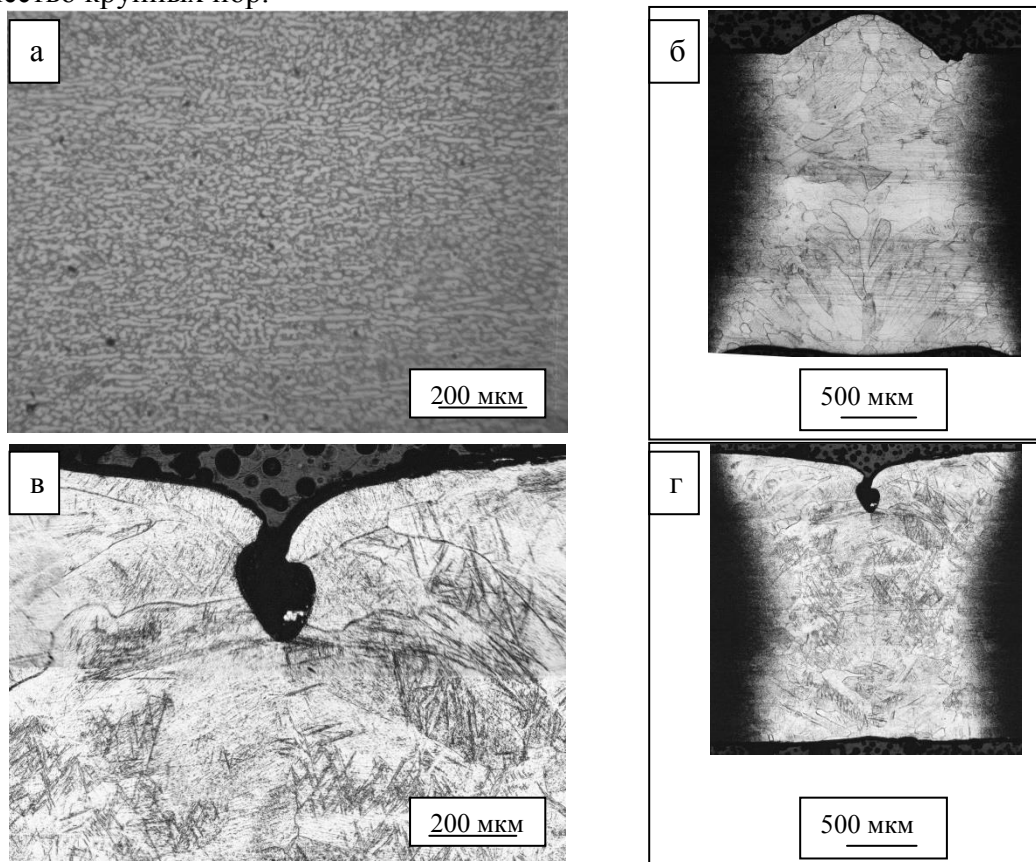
Структура сварных соединений титанового сплава BT23: а - зона основной металл без применения обработок; б - панорама сварного шва без применения обработок; в - зона сварного шва BT23 после ТМО2; г) - панорама сварного шва после ТМО2
